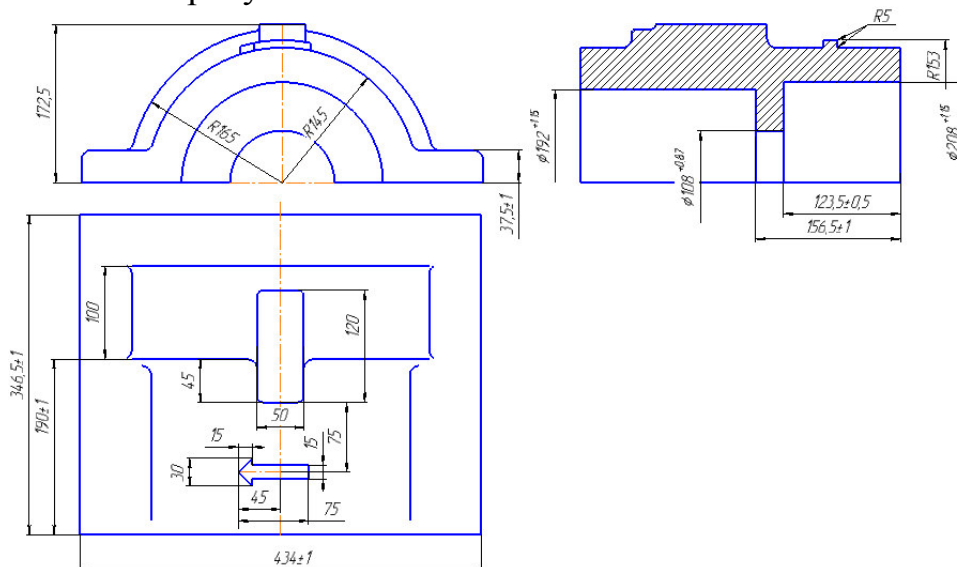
Отливка детали "Крышка подшипникового узла"
